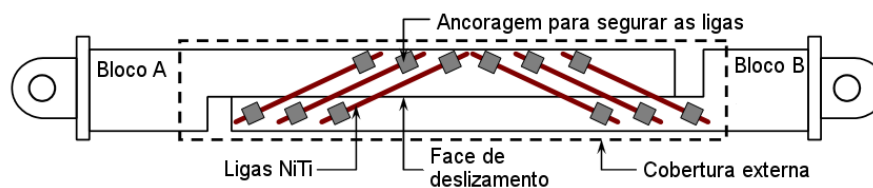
Dispositivo constituído por 2 peças metálicas unidas por LMF, adaptado de [49]
